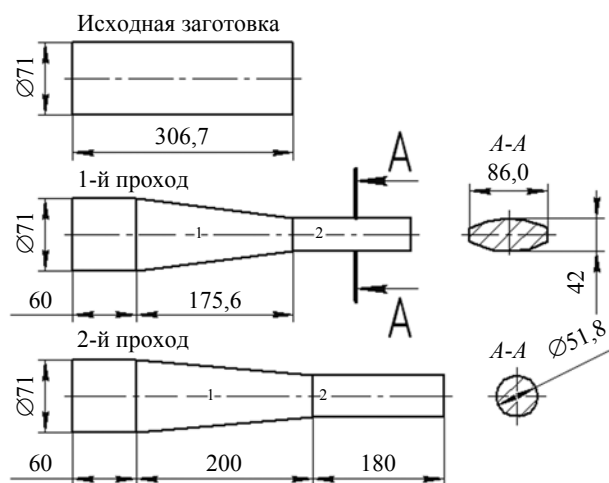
Исходная заготовка и переходы вальцованной заготовки
